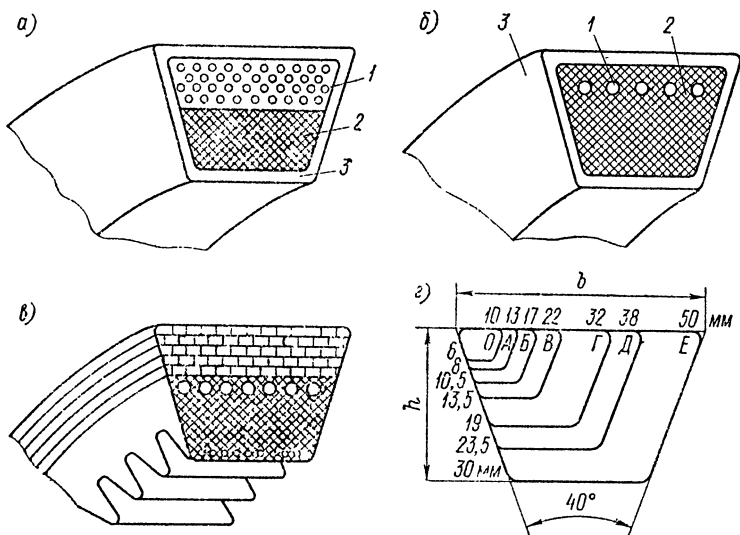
Клиновые приводные ремни: а — кордтканевые; б — кордшнуровые; в — кордшнуровые зубчатые; г — типы клиновых ремней
